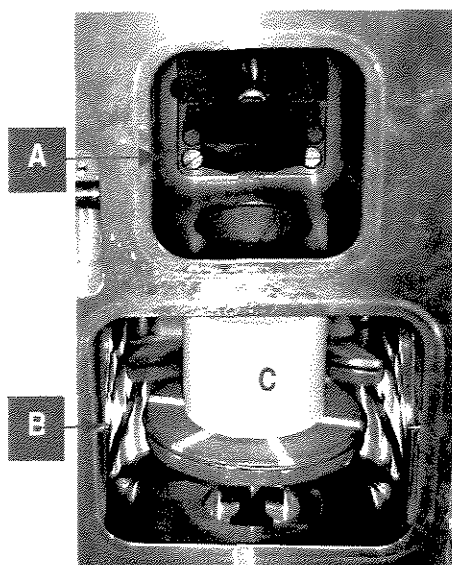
Vista interna da máquina de fundição: (A) câmara superior de fundição; (B) câmara inferior; (C) molde de revestimento.
